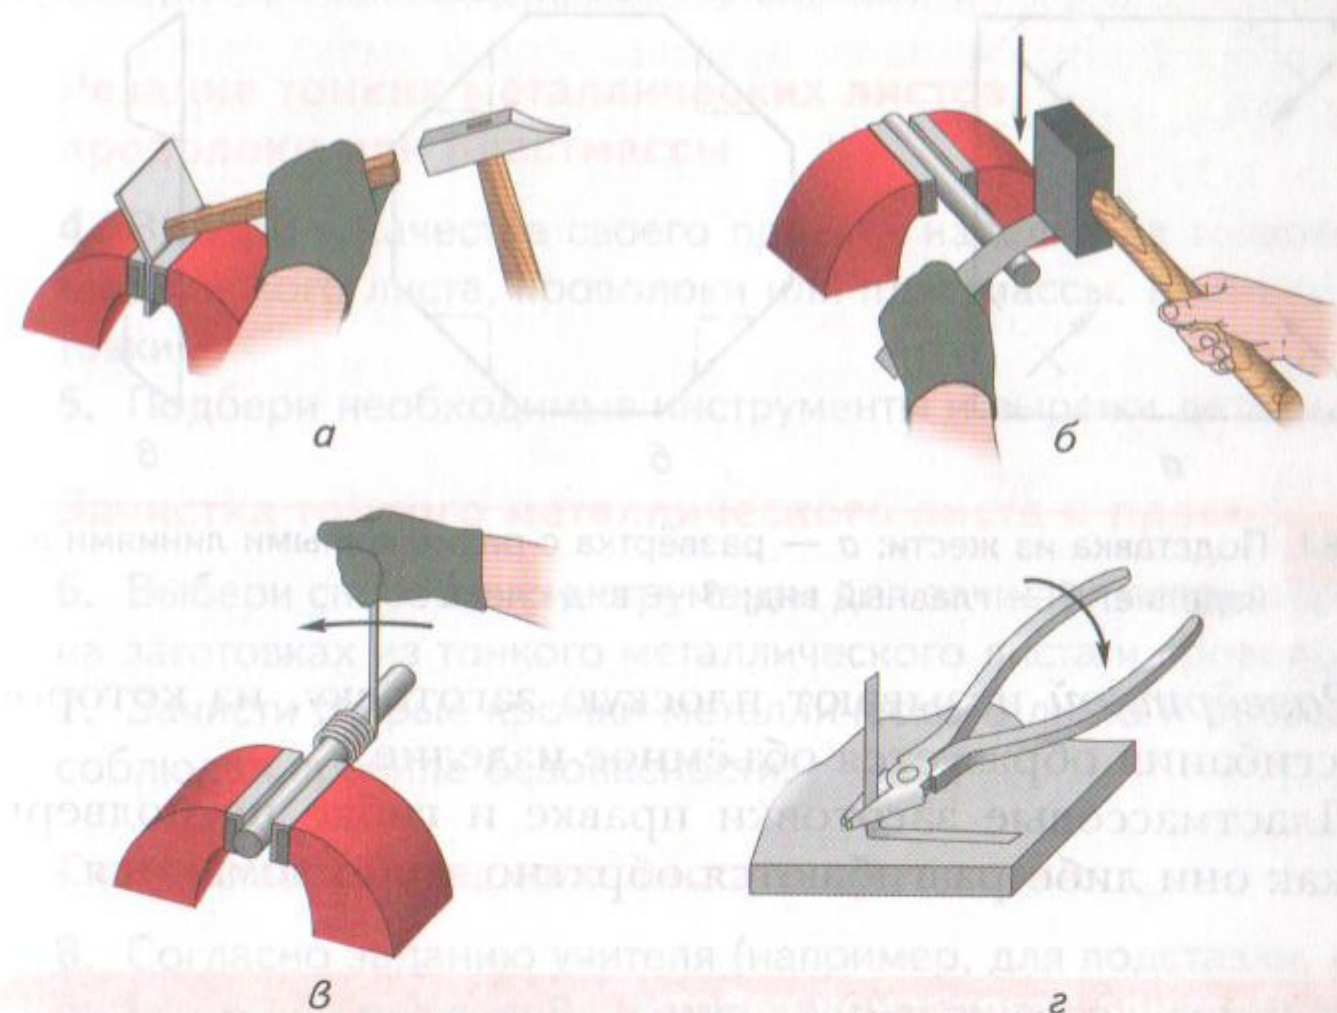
Гибка заготовки: а — в тисках; б — на оправке; в — навивкой проволоки на оправке; з — круглогубцами
